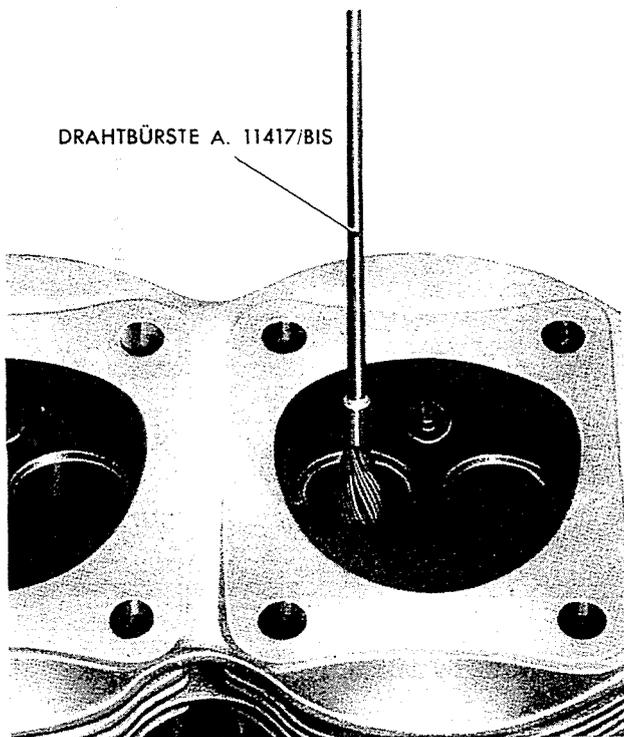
Bohrungen der Ventilführungen mit Drahtbürste A. 11417/bis reinigen.
